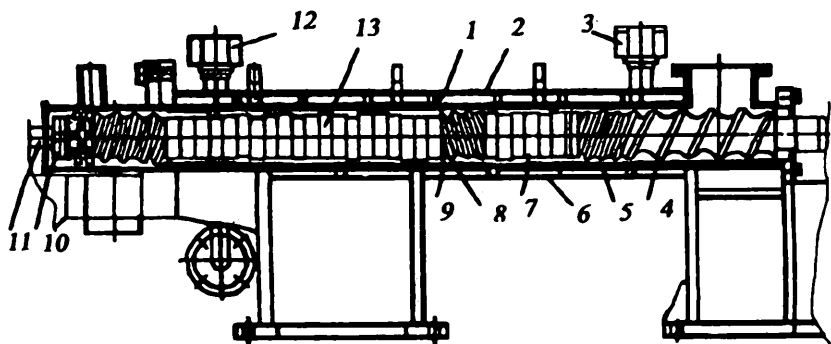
Смеситель для непрерывного клееприготовления типа СН-100
